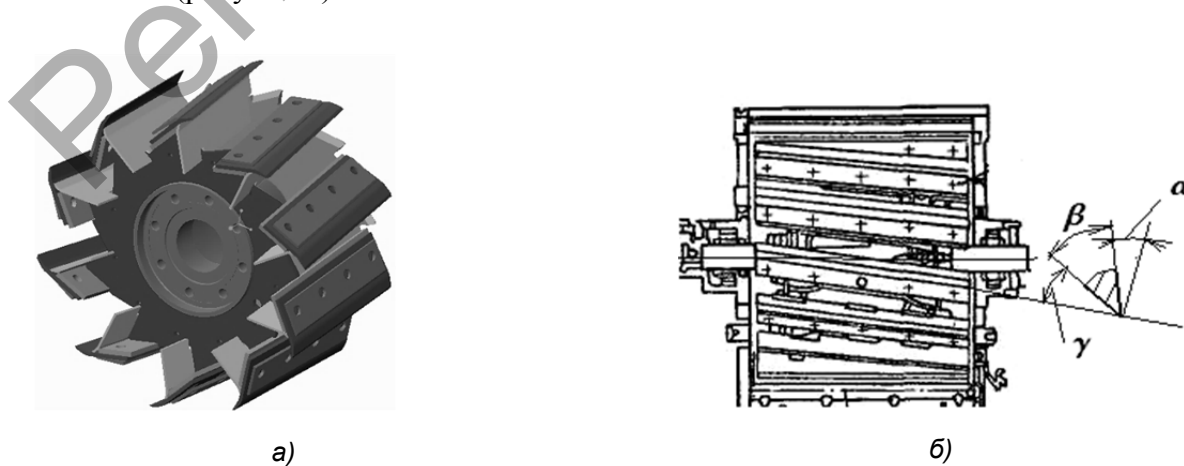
Общий вид измельчающего барабана кормоуборочного комбайна (а), углы режущего лезвия (б)
